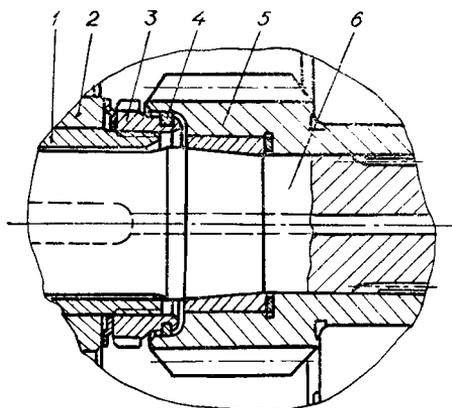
Уплотнение зазора между валами переднего и заднего хода реверс-редуктора:
